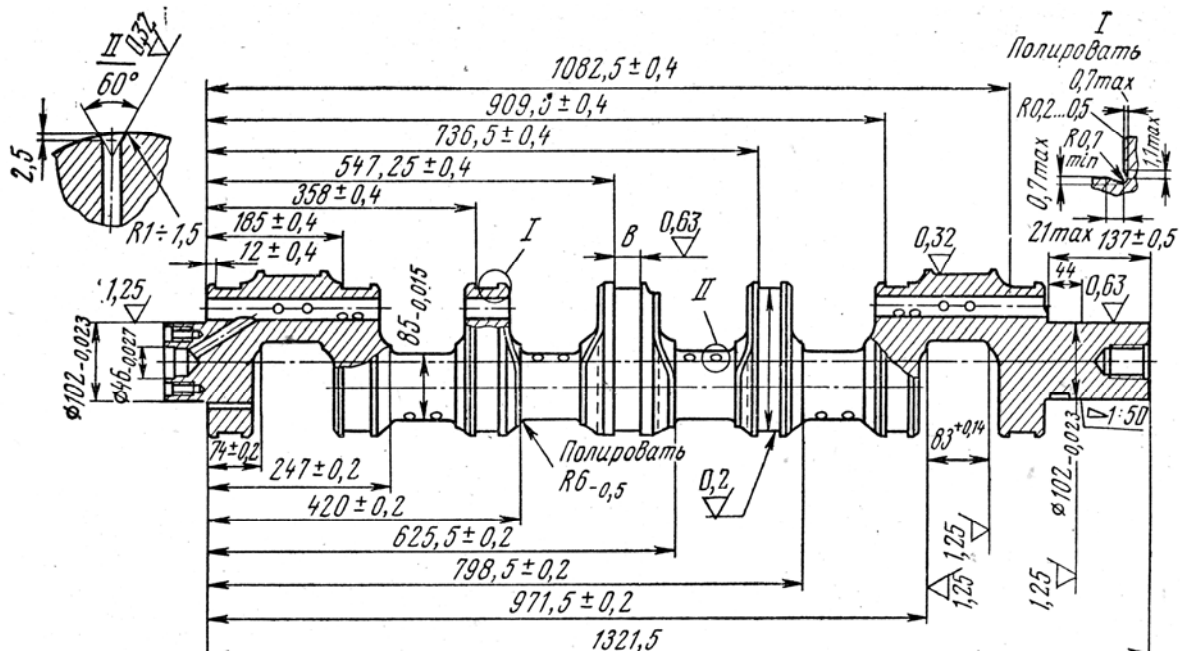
Коленчатый вал двигателя ЯМЗ-240НБ
